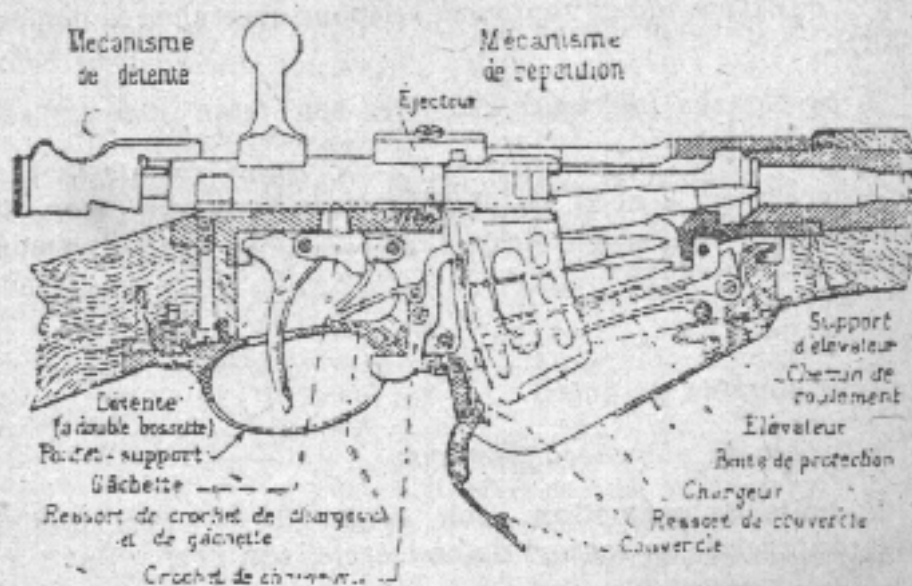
Mécanismes. (Vue d'ensemble, en coupe.)
